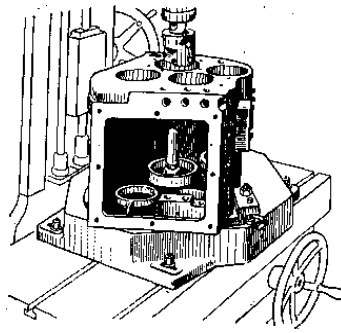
Розточування поверхні отвору в корпусі коробки передач трактора на вертикально-розточувальному верстаті 278Н.
